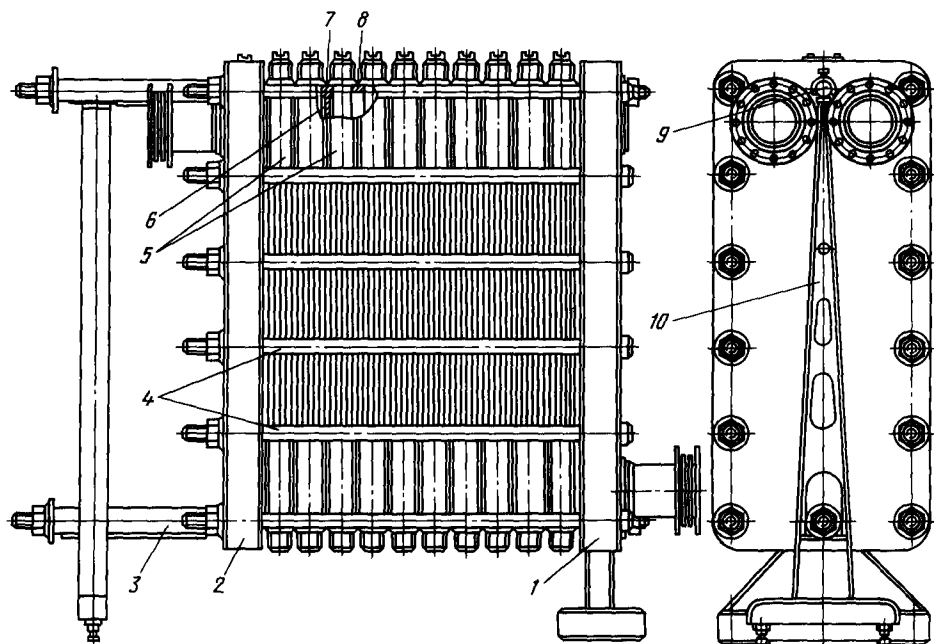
Пластина́тый теплообменник со сварными блоками на двухопорной раме:
